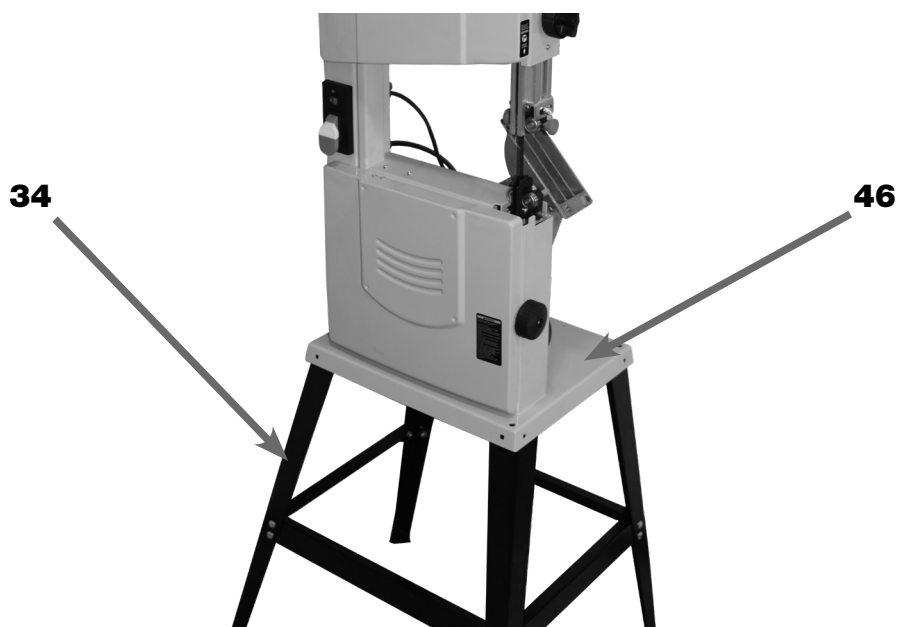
Montagem da Estrutura sobre o Conjunto da Base de Apoio
